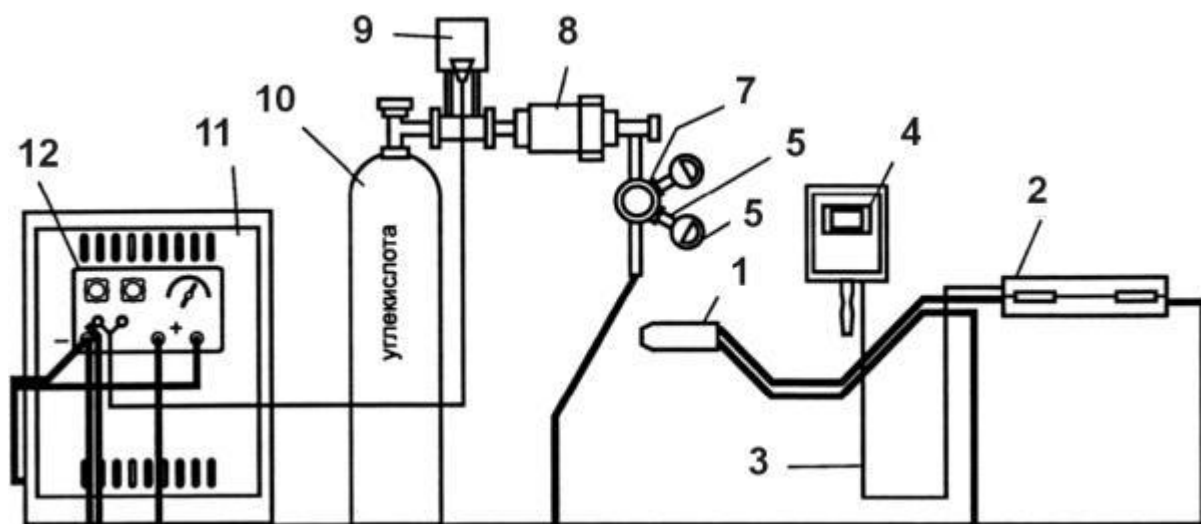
Схема поста полуавтоматической сварки тонкой электродной проволокой в углекислом газе: 1 – держатель; 2 – подающий механизм; 3 – кнопка включения; 4 – защитный щиток; 5 – манометр на 6 атмосфер; 6 – переходной штуцер для установки манометра; 7 – редуктор кислородный с манометром высокого давления; 8 – осушитель газа; 9 – подогреватель газа; 10 – баллон с углекислым газом; 11 – сварочный выпрямитель; 12 – пульт управления
